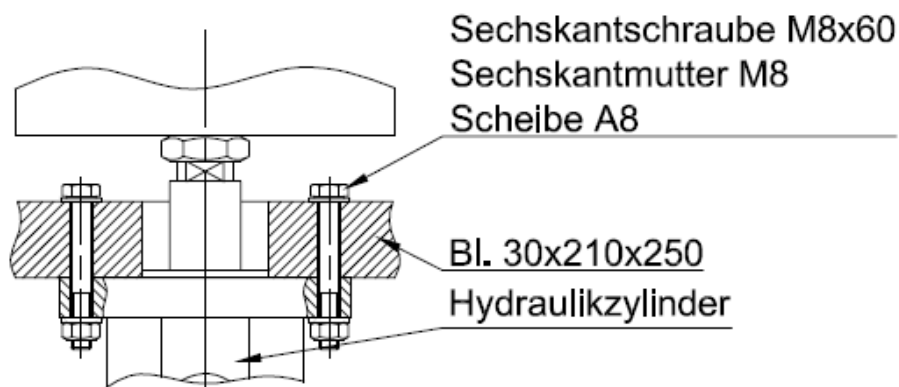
BG4; Detail Befestigung Hydraulikzylinder
